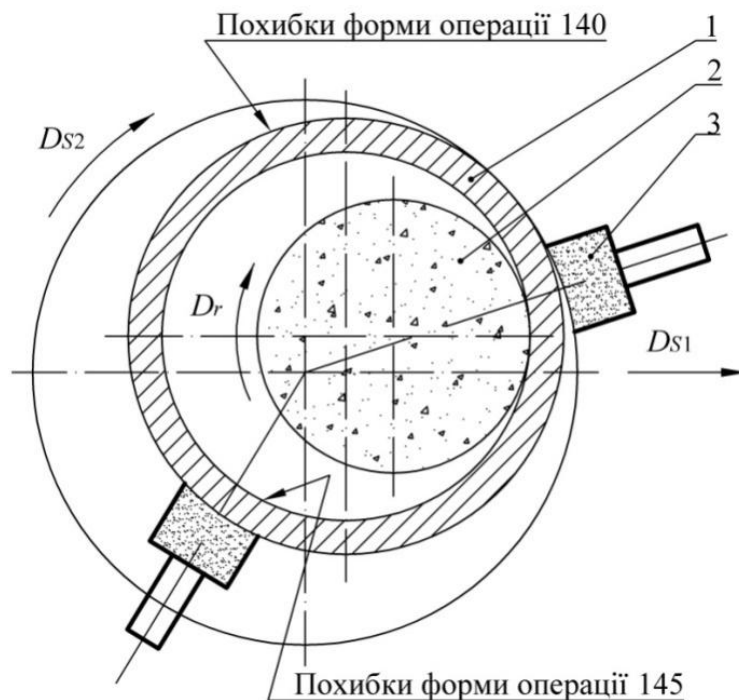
Схема шліфування доріжки кочення кільця зовнішнього: 1 – заготовка кільця; 2 – головка шліфувальна; 3 – опори
